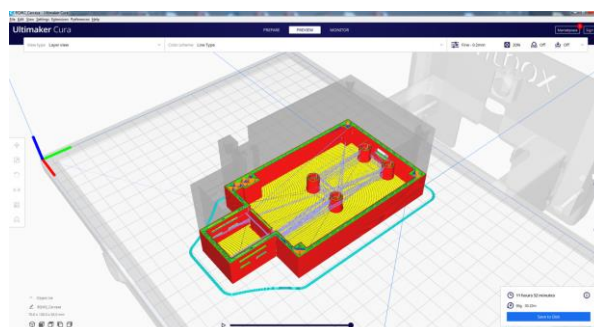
Vista de la carcasa que muestra el proceso de impresión.
